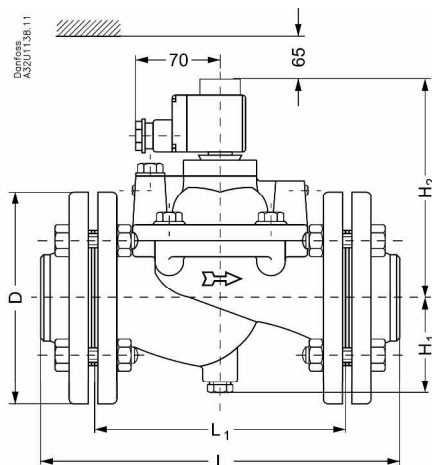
Габаритные и присоединительные размеры соленоидного клапана.
